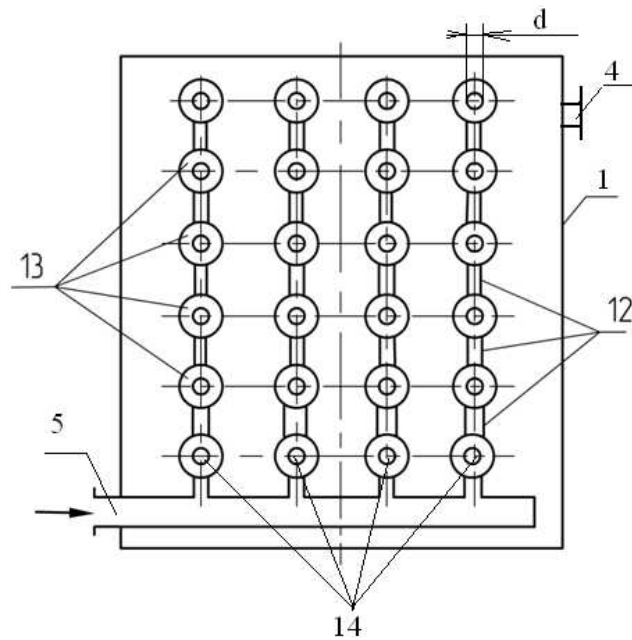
Поперечный разрез по Б-Б колонны с насадкой
